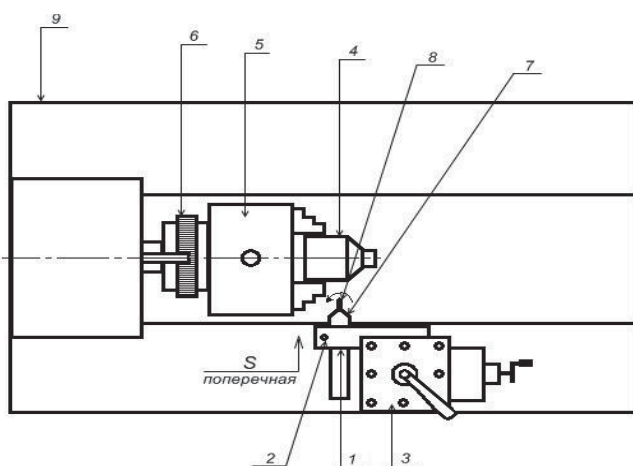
Схема универсального узла для обработки отверстий и пазов на диаметре детали
